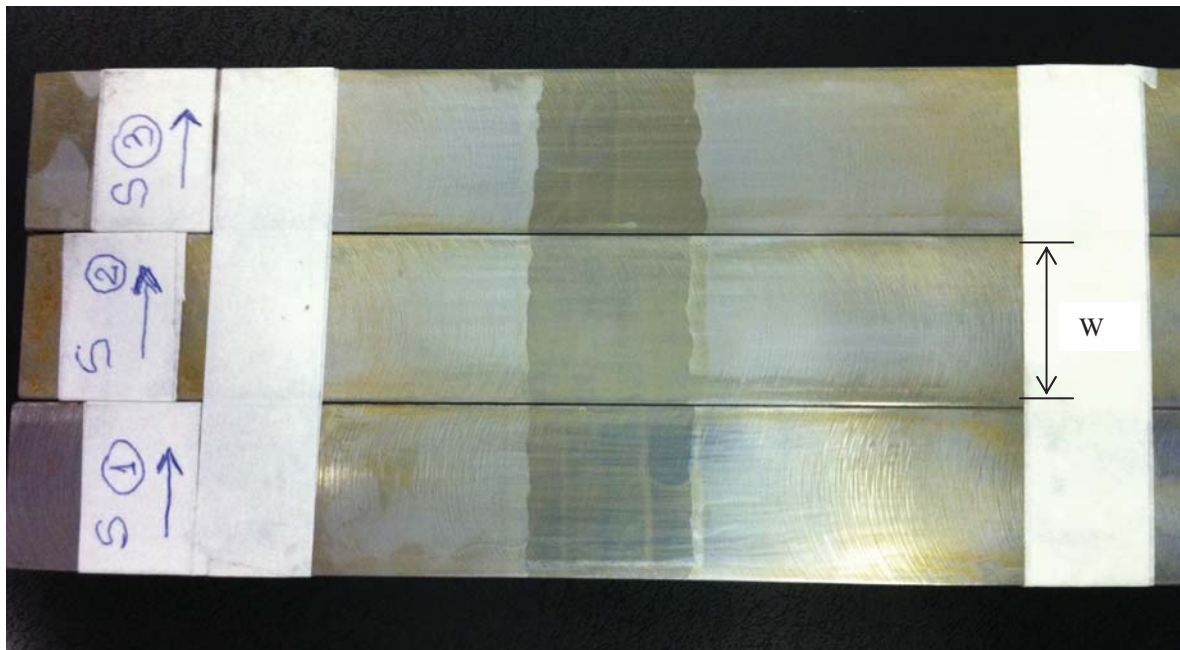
Corpos de prova SE (B) (solda) após o ataque químico. ($W = 28 \text{ mm}$)
